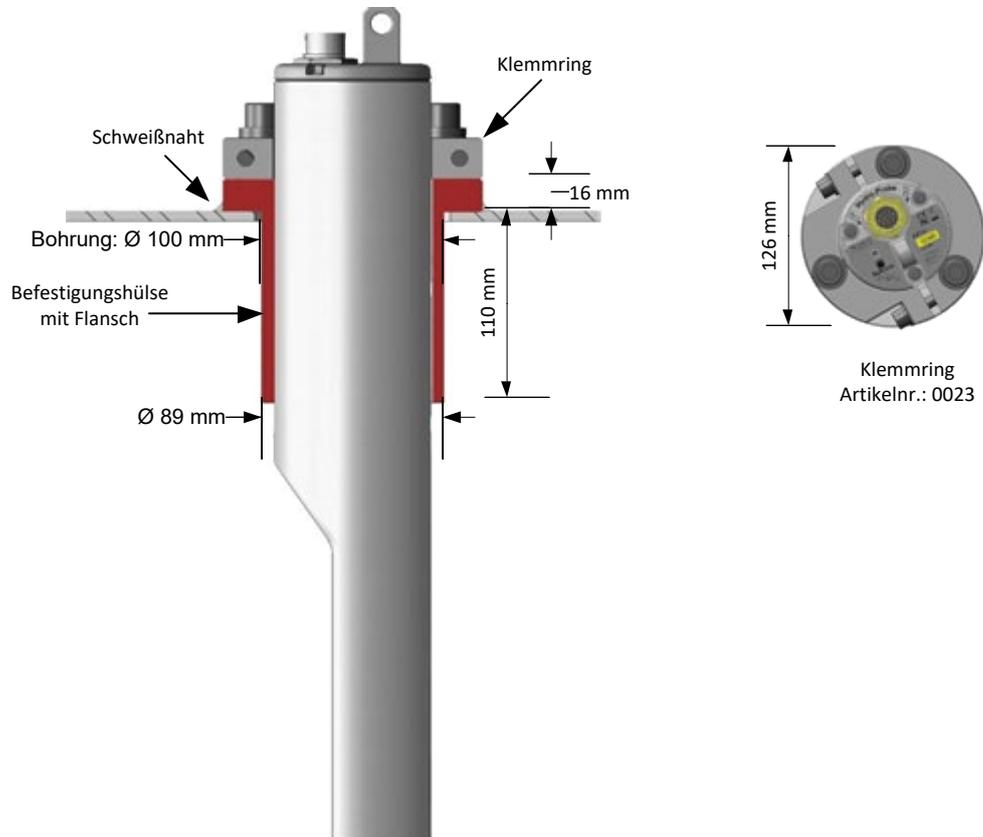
Befestigungshülse mit Flansch (Artikelnr. 0024A)
